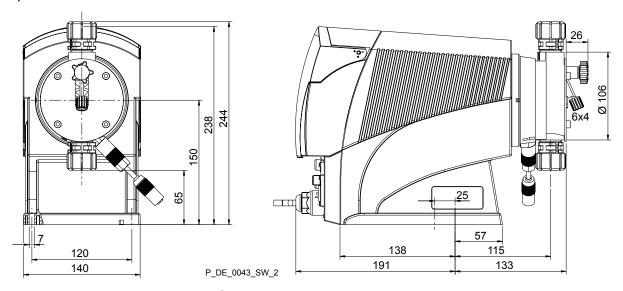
Hoja de dimensiones del tipo delta® 0450 - 0280, versión de materiales PV; dimensiones en mm
